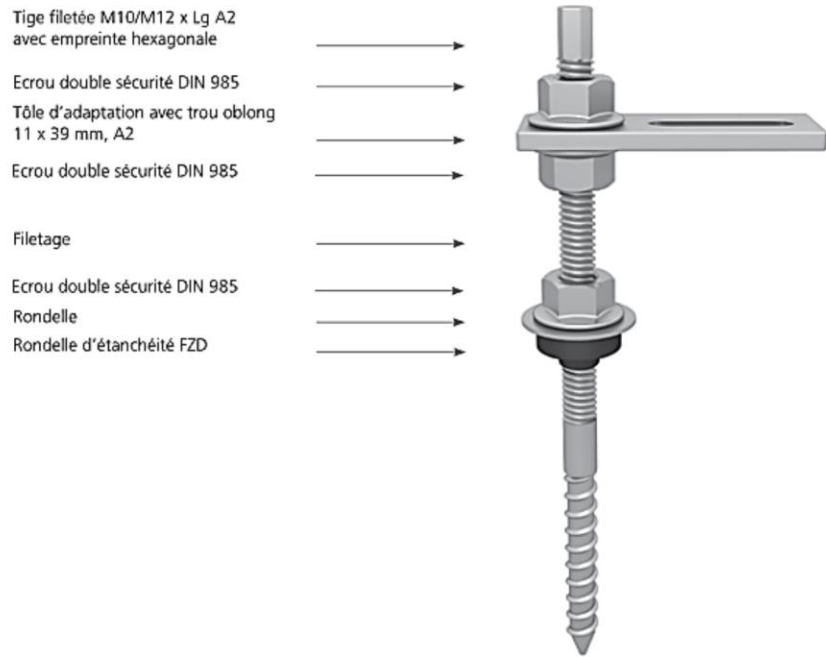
Kit tire-fond de fixation sur tôle ondulée
